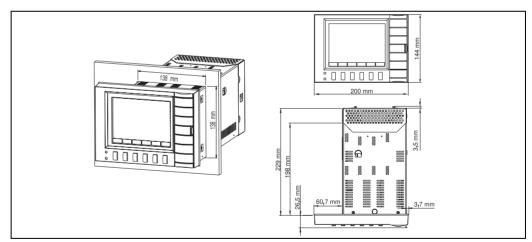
Dimensioni di montaggio a fronte quadro con frontalino pressofuso
